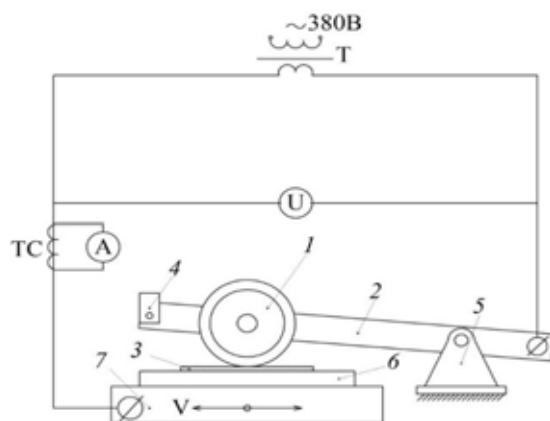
Схема установки для формування на сталевій поверхні високовуглецевого шару
